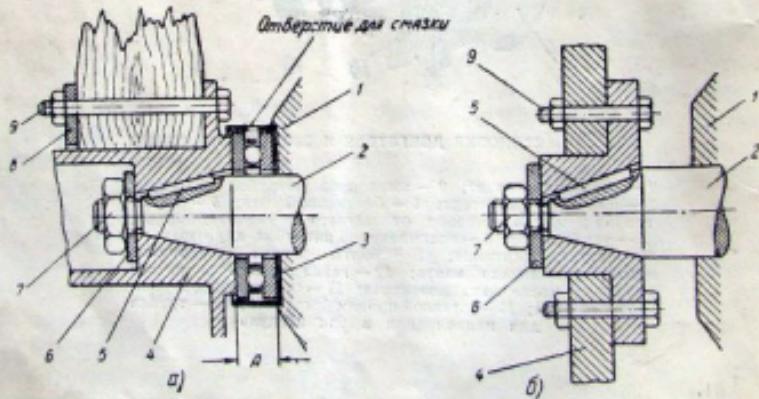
Схема установки втулки винта на хвостовике коленчатого вала:
